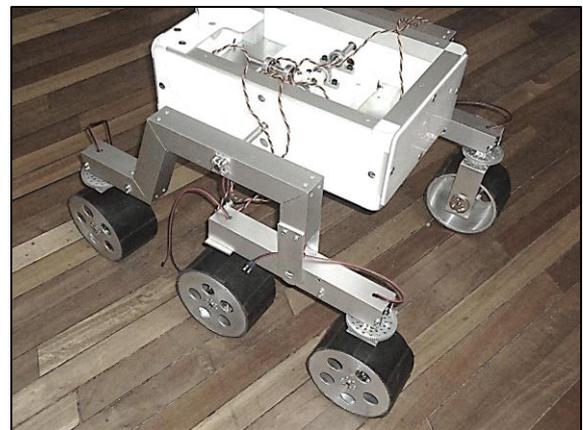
Resultado final del ensamblaje mecánico del robot.
